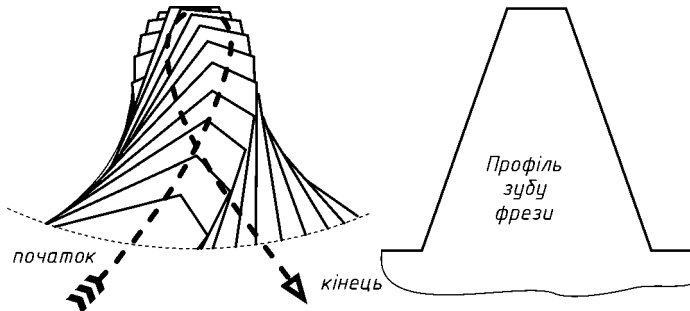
Фрезерування зубчатого колеса черв'ячною фрезою
